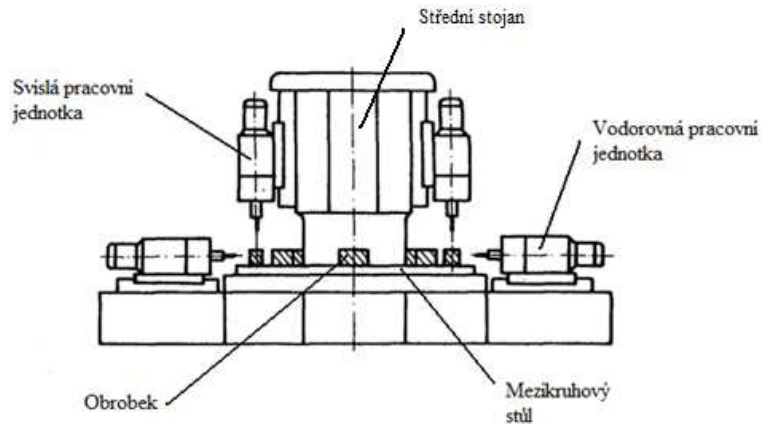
JÚS s otočným stolem kruhovým [11]
